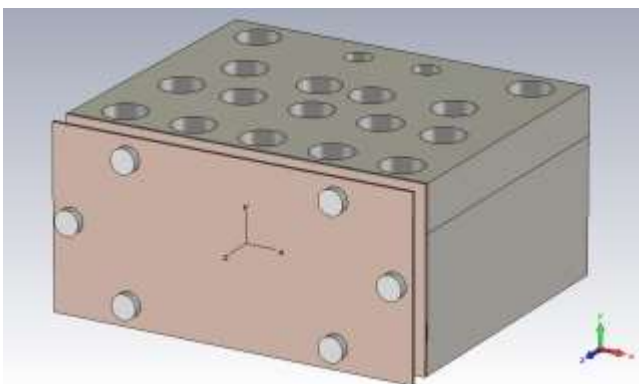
Construcción: sustratos y plancha de *foam* para plano E
